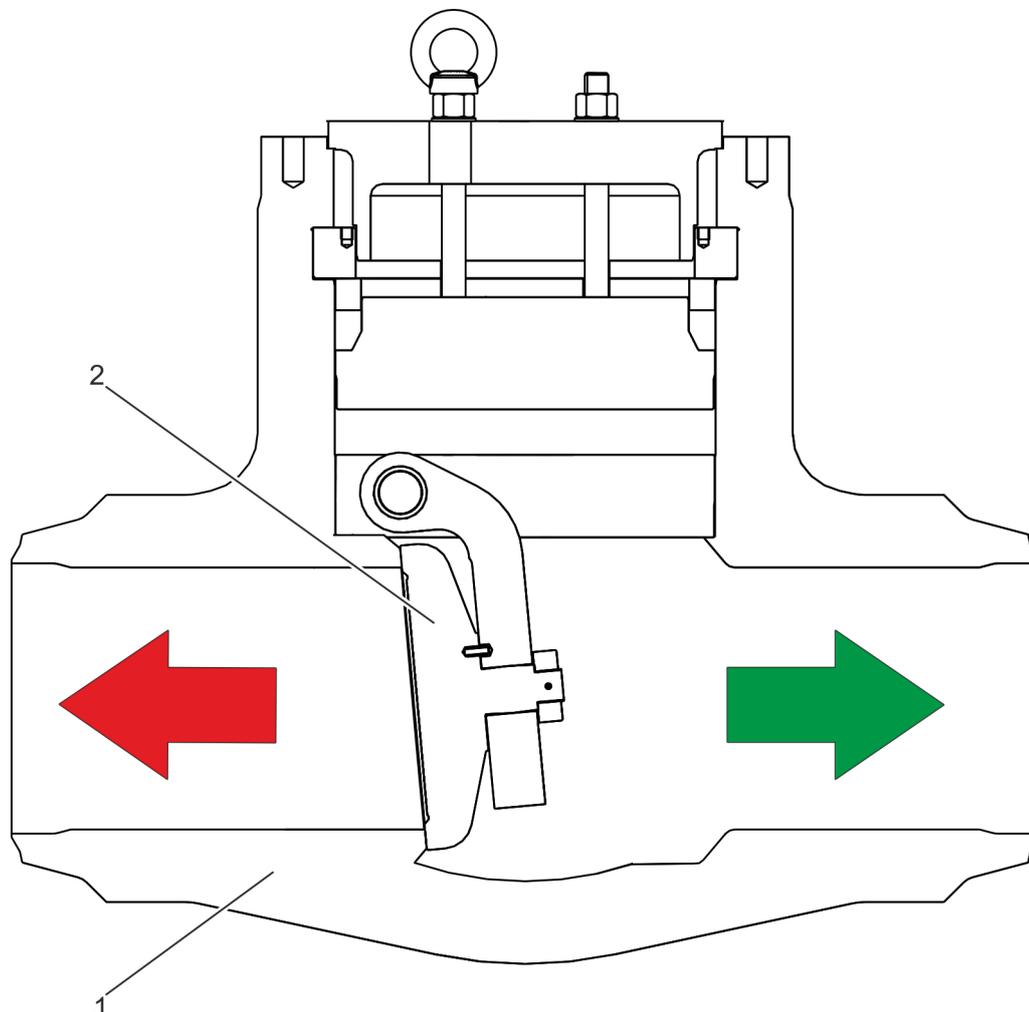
Vue en coupe du clapet anti-retour à haute pression
